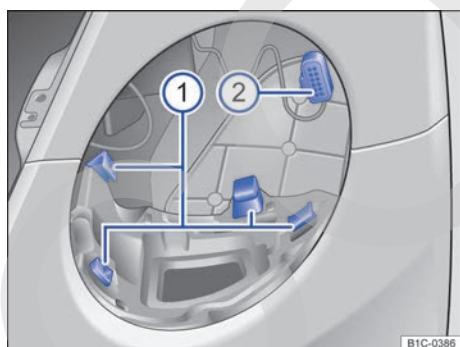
Guías ① y conector ② para el montaje del faro izquierdo.
